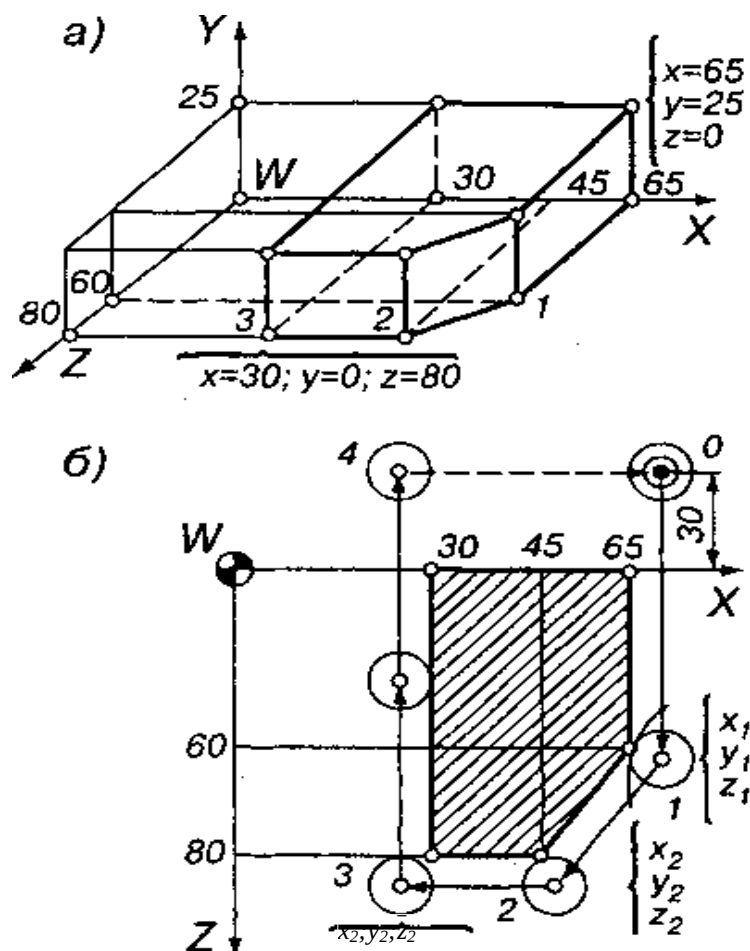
Схема определения координат опорных точек контура детали (а) и траектории движения центра инструмента (б)
